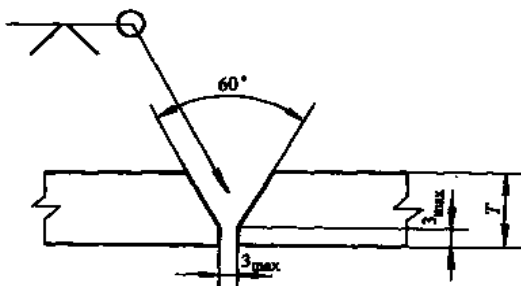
管材对接接头焊接工艺评定试件形式和尺寸
